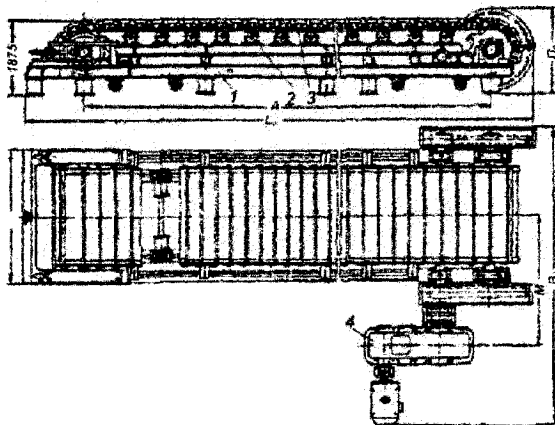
Пластинчатый питатель типа ПТ:
